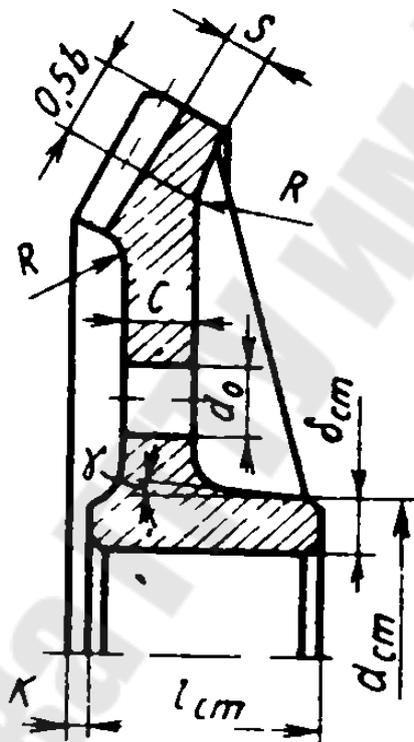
Конструкция диска, обода и ступицы колеса конического
